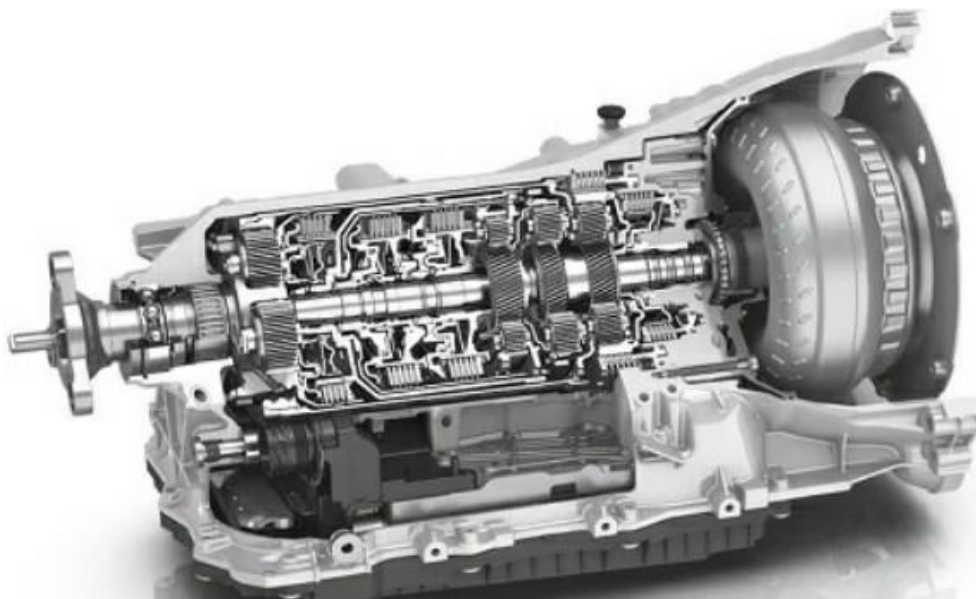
Схема конструкції коробки-автомат класичної конструкції
